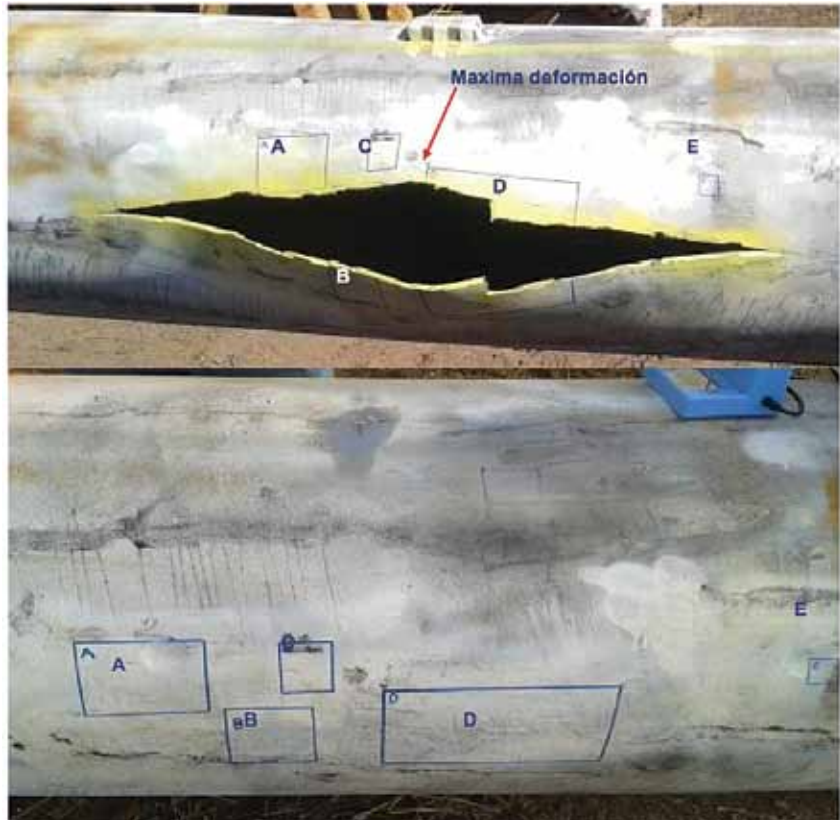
Grupo de fisuras en el caño extraído para la prueba hidráulica a rotura.
